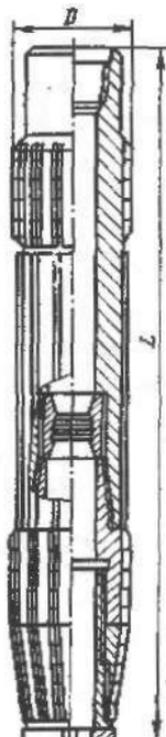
Скважинный фрезер райбер типа ФРЛ
